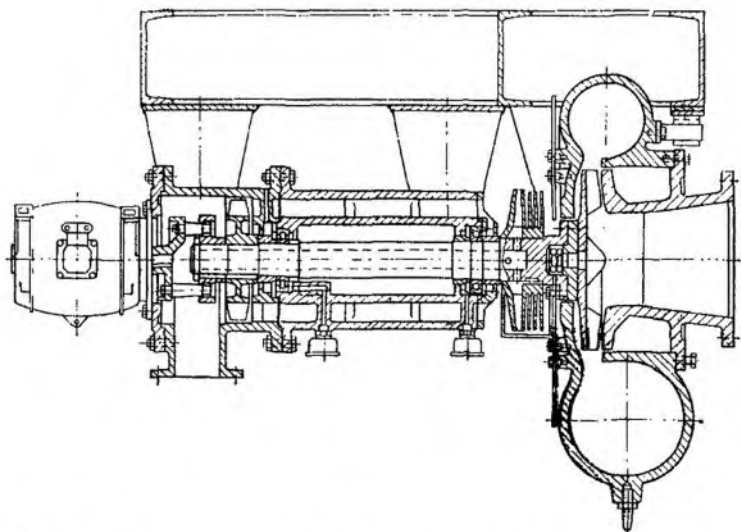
Одноступенчатый турбокомпрессор без холодильника
